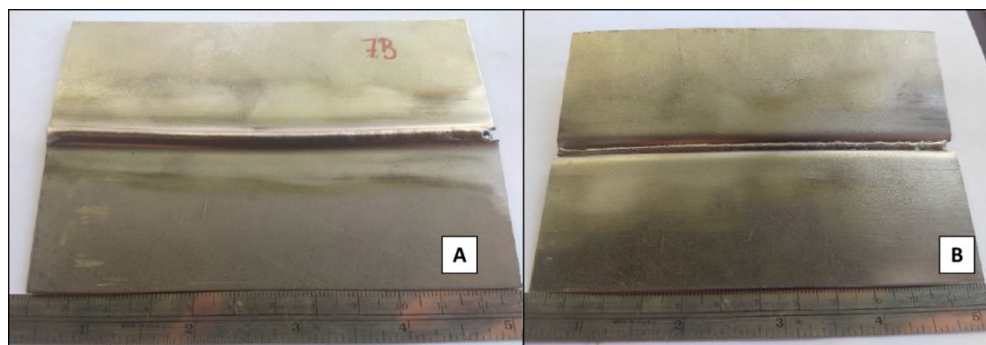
Condição 7 de soldagem GMAW. A) vista de cima da chapa soldada B) Vista do verso da solda (Próprio autor)
